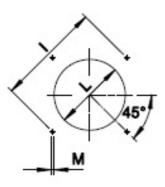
Dimensioni ingombro FGP 190/M - FGP 250/M
